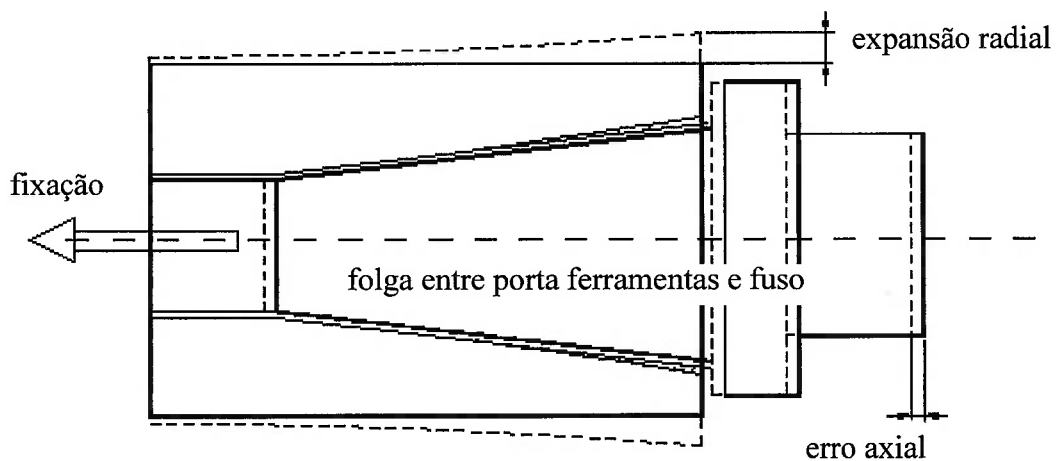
efeito do desbalanceamento entre o porta ferramenta e o sistema de fixação (adaptado de BILZ Werkzeugfabrik [50])
